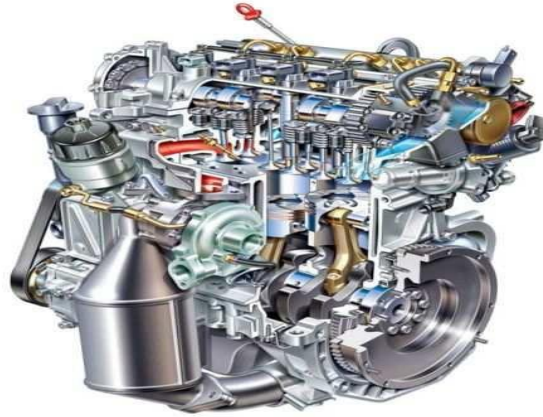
Vue éclatée d'un moteur Diesel moderne[11]
